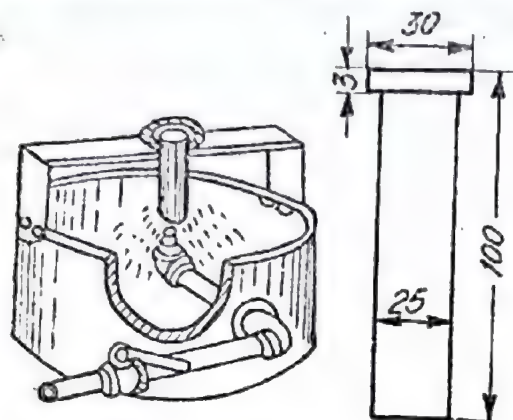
Dispozitivul și epruveta pentru călire frontală.
